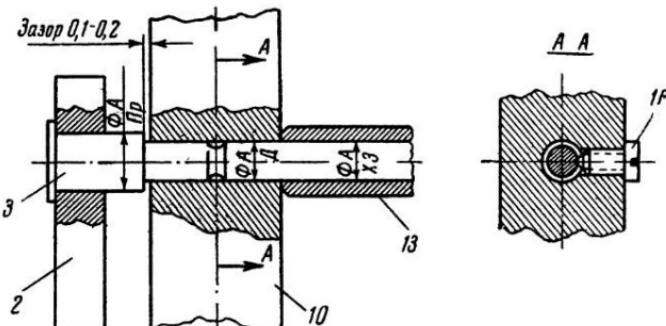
Модель кулачкового механизма (схема соединения деталей ведущего вала): 2 — кулачок; 3 — вал привода; 10 — стойка; 13 — упорная втулка; 16 — стопорный винт.
